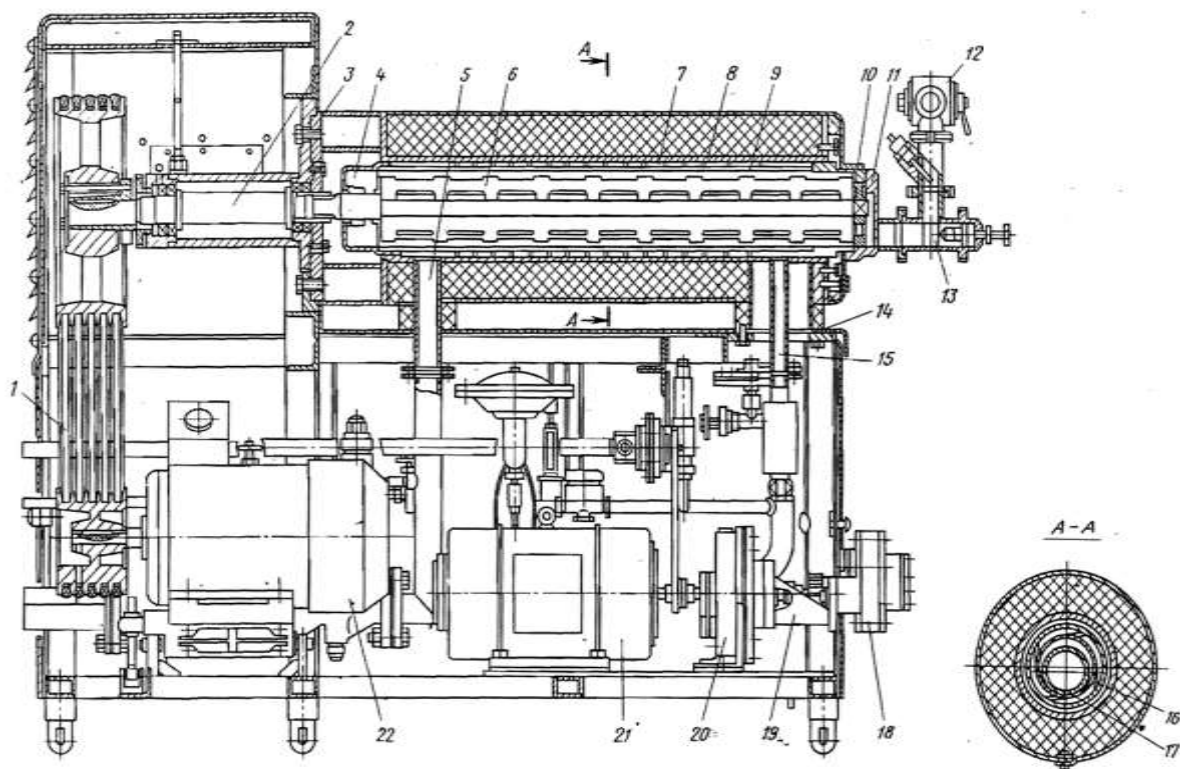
Общий вид цилиндра фризера марки Б6-ОФШ:
